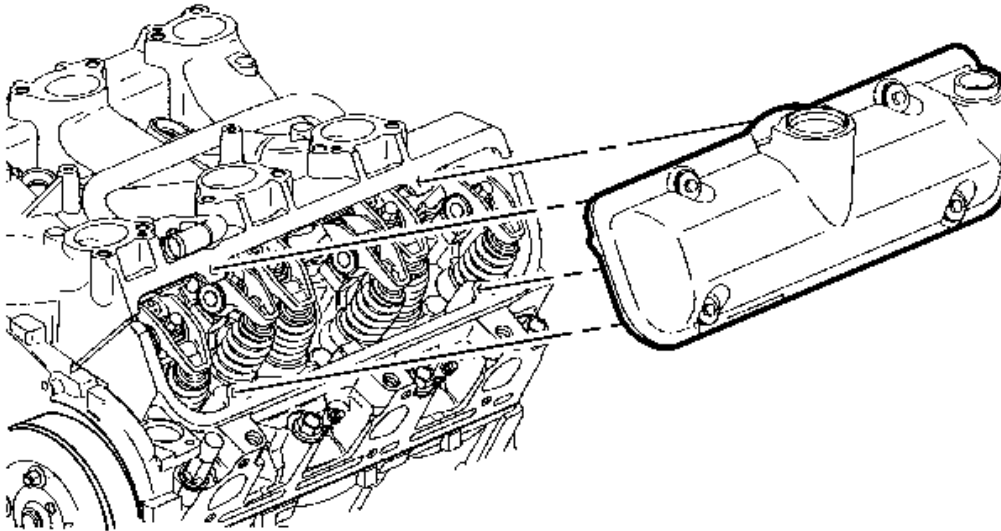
Vista de la cubierta del balancín de la válvula - Izquierda
